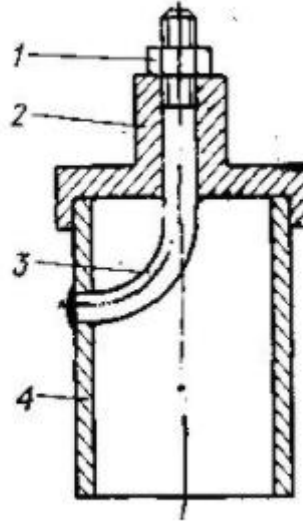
Приварка шпильки до корпусу ковпачка.
